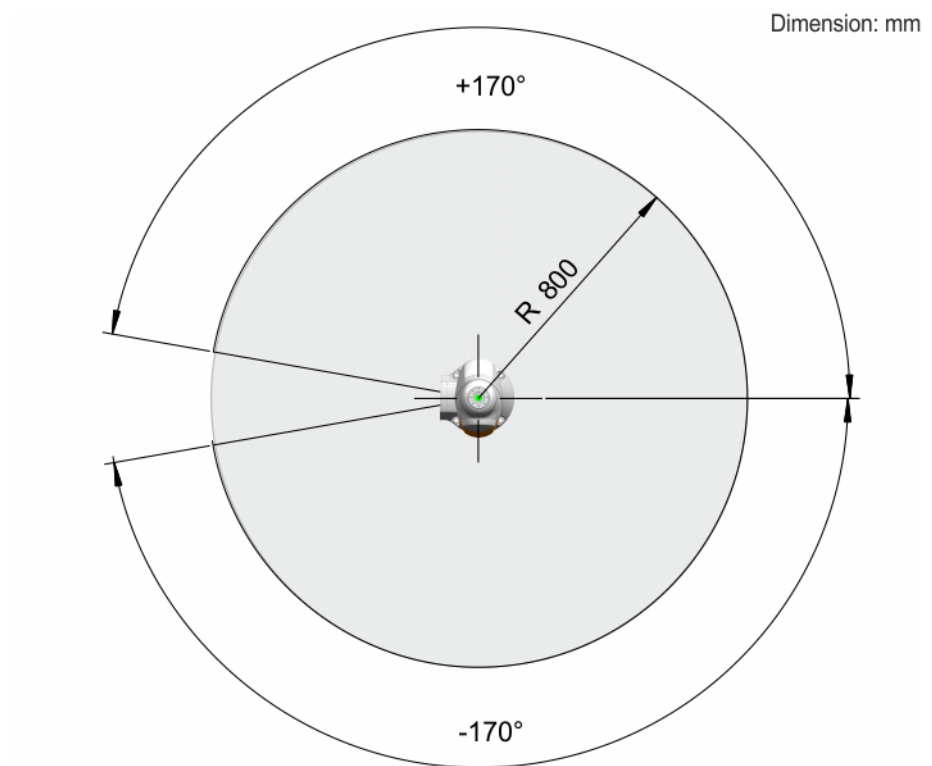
LBR iiwa 7 R800 工作区域, 俯视图
